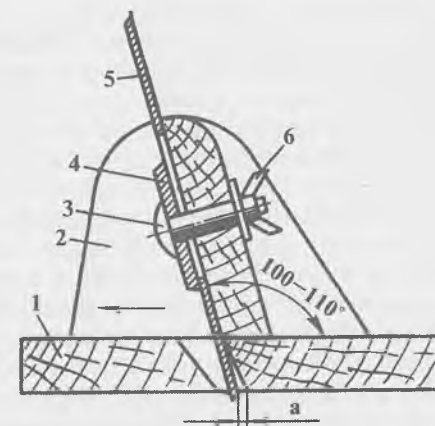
Схема цикли с корпусом: 1 — подошва; 2 — колодка; 3 — винт; 4 — прокладка; 5 — нож; 6 — гайка
